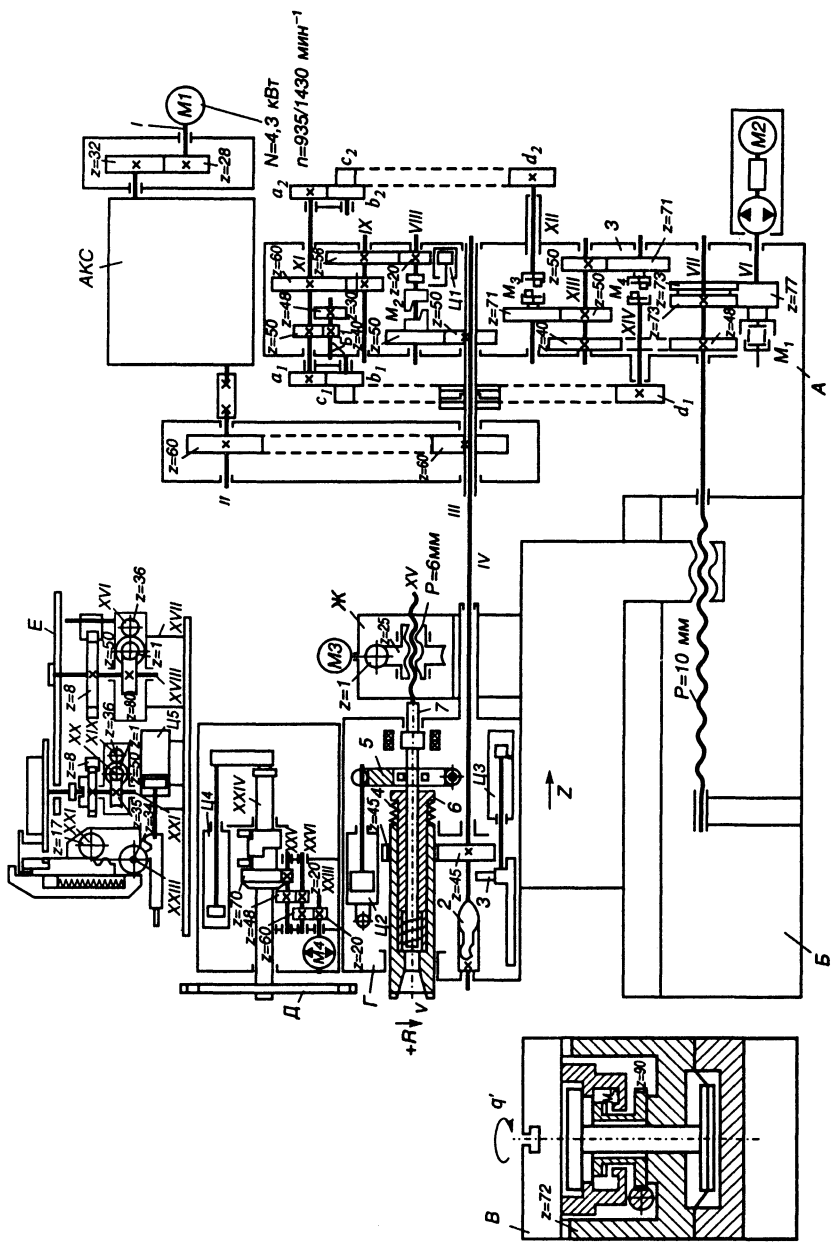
Кинематическая схема агрегатного станка МА299Ф2 с ЧПУ
